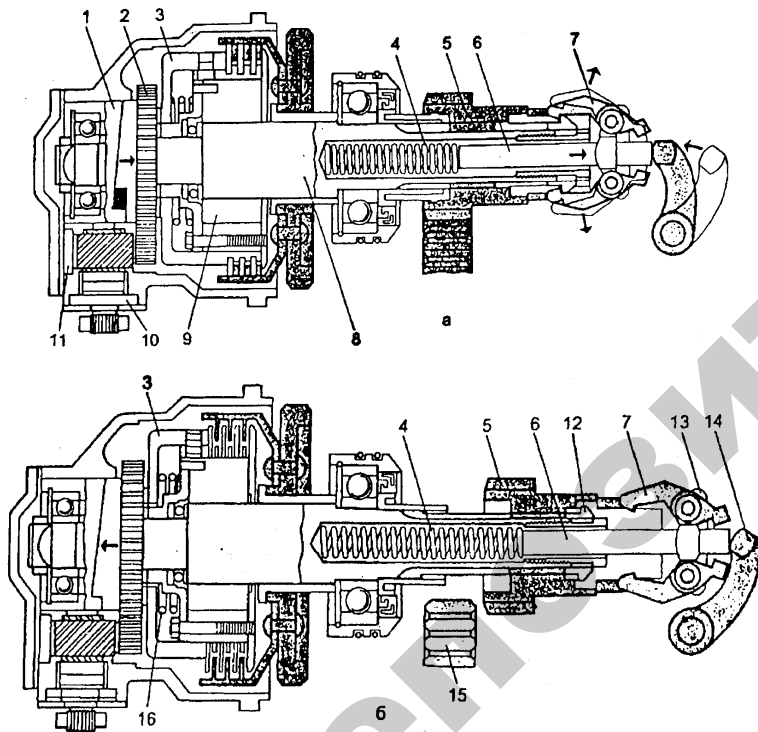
Схема редуктора пускового двигателя П-10УД
